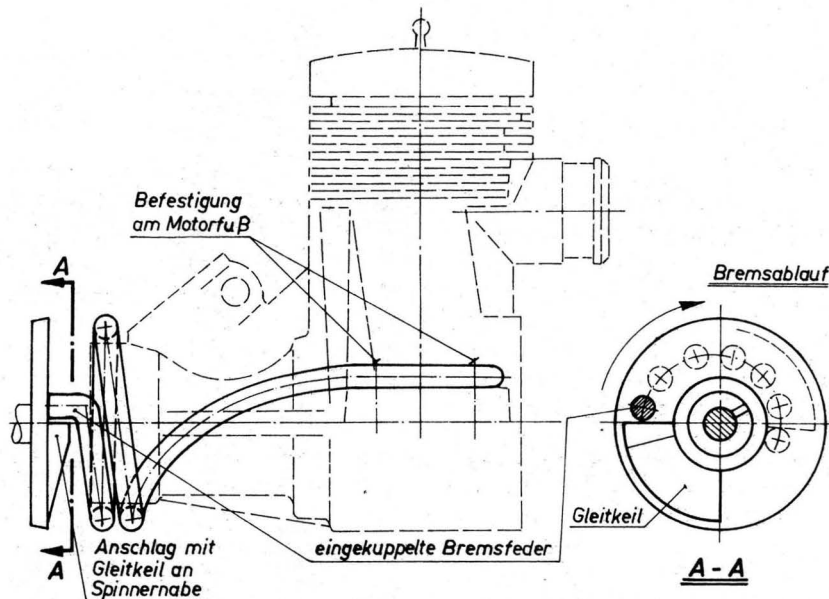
Motorbremse mittels Spiralfeder des Vizeweltmeisters Verbitzki
